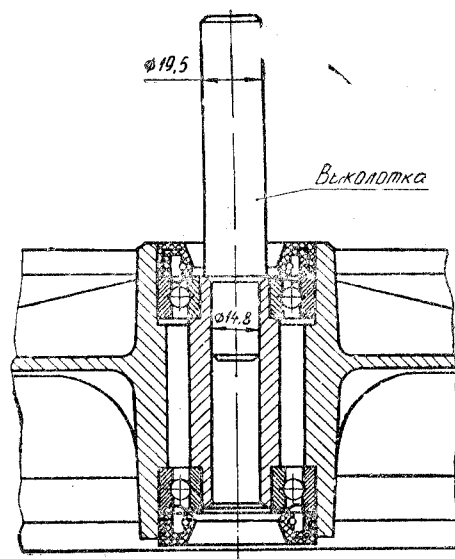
Выпрессовка подшипников и сальников из ступицы колеса
